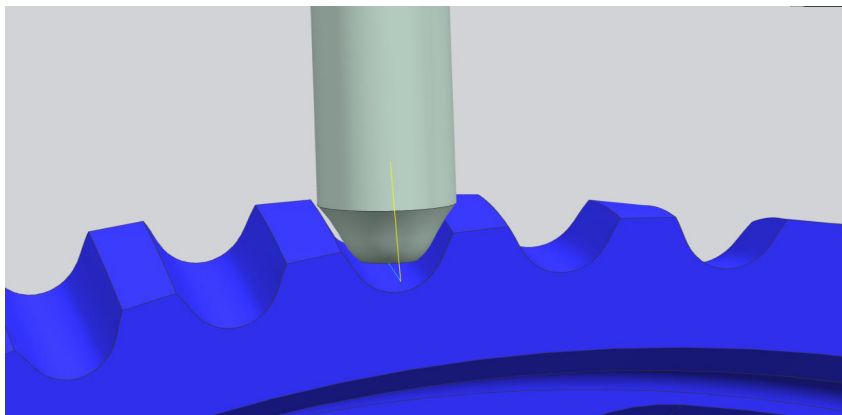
Движение профильного инструмента при чистовой обработке колеса
